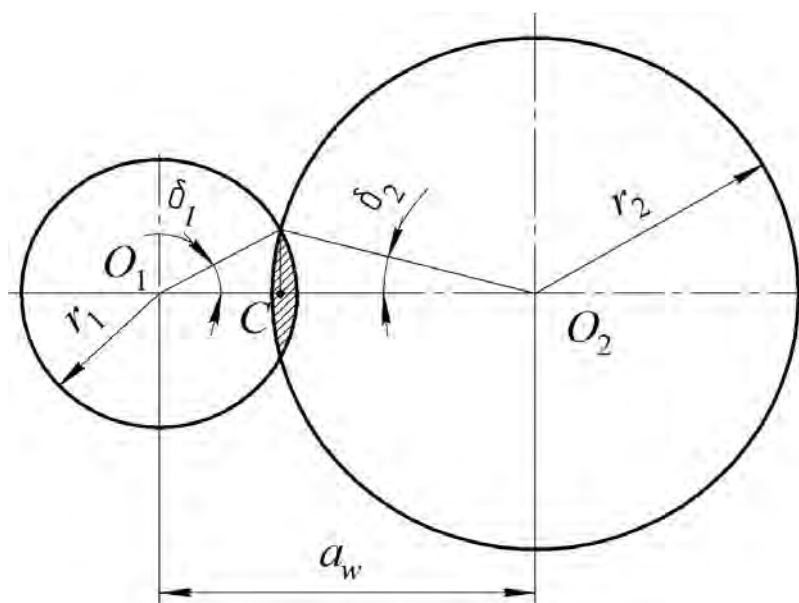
Схема для определения площади поверхности контакта витков резьбы
